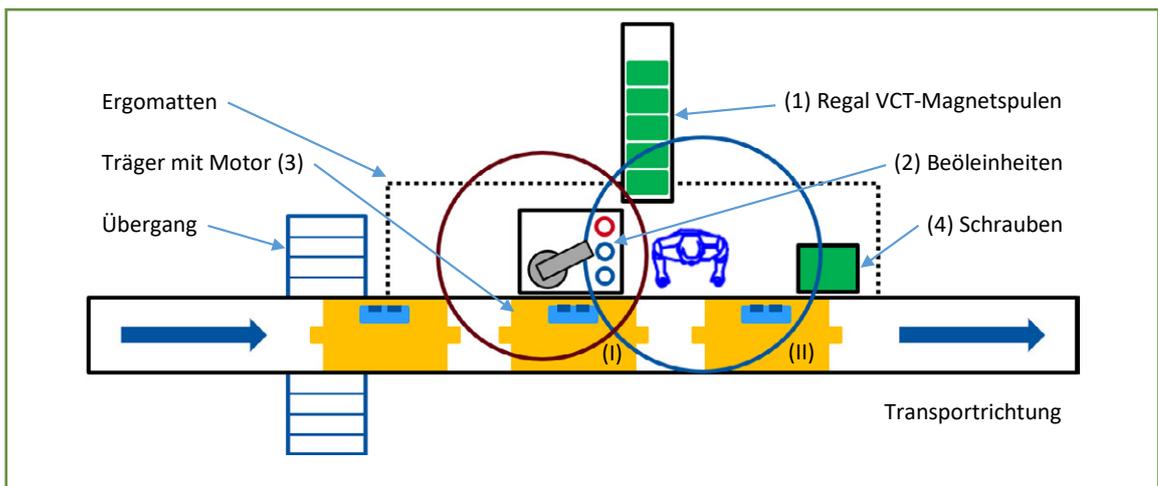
Layout der geplanten Montagestation mit kollaborierendem Roboter
